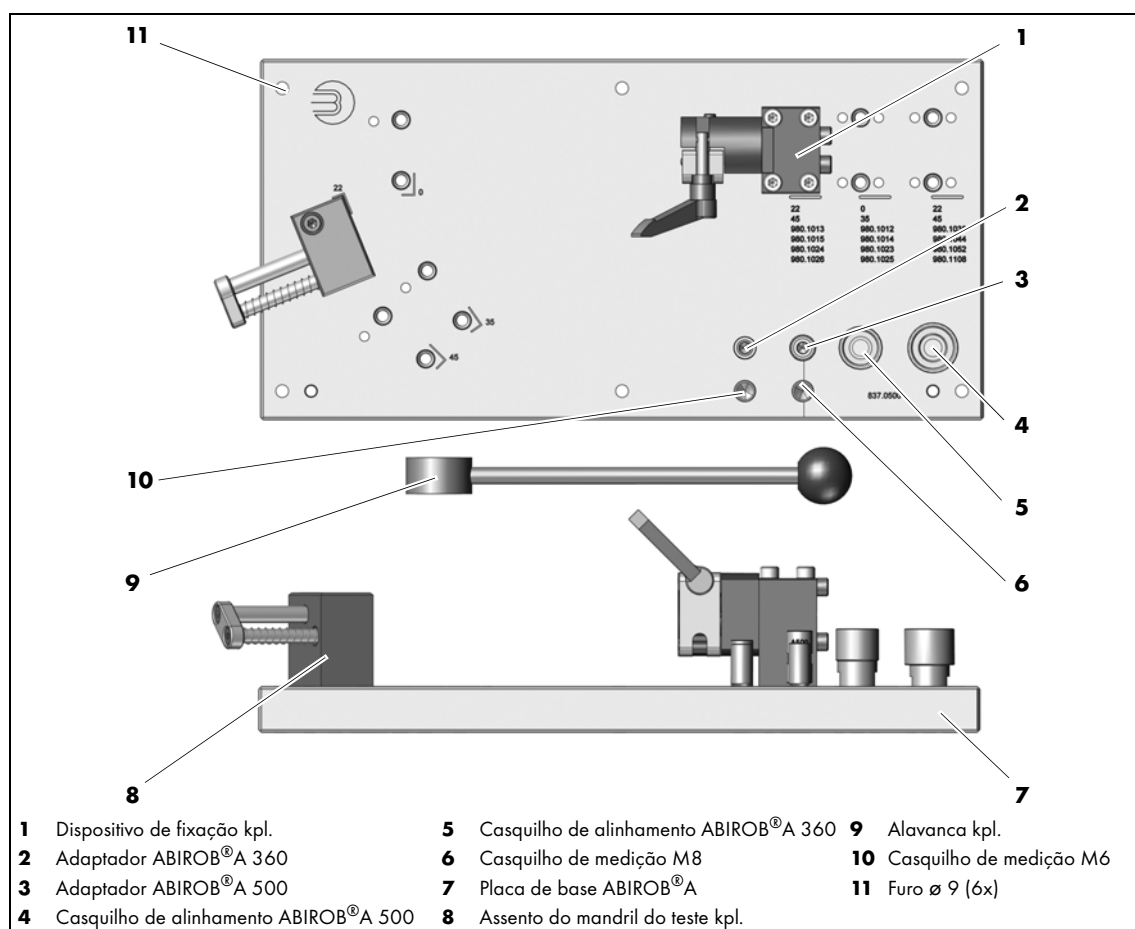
Instalar o dispositivo de ajuste ABIROB® A
